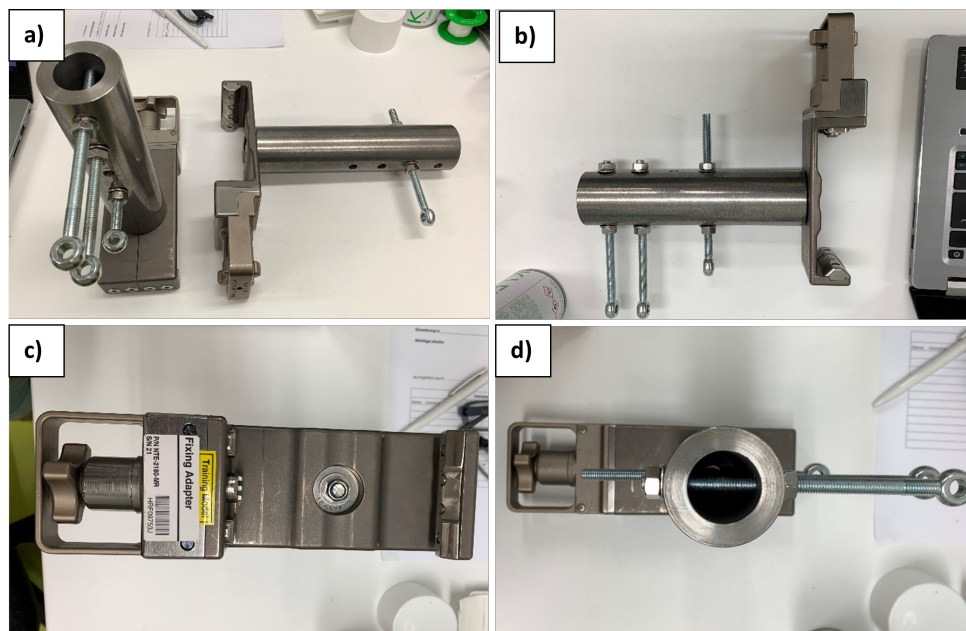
a) Beide Stahlaufsätze mit zugehörigen Fixing-Adaptern und Augenschrauben zur Befestigung der Federn und Dämpfer. b) rechter Aufsatz in der Seitenansicht. c) Rückansicht der Befestigung des Aufsatzes auf dem Fixing Adapter. d) Vorderansicht des Aufsatzes. Quelle: Eigene Abbildung.
